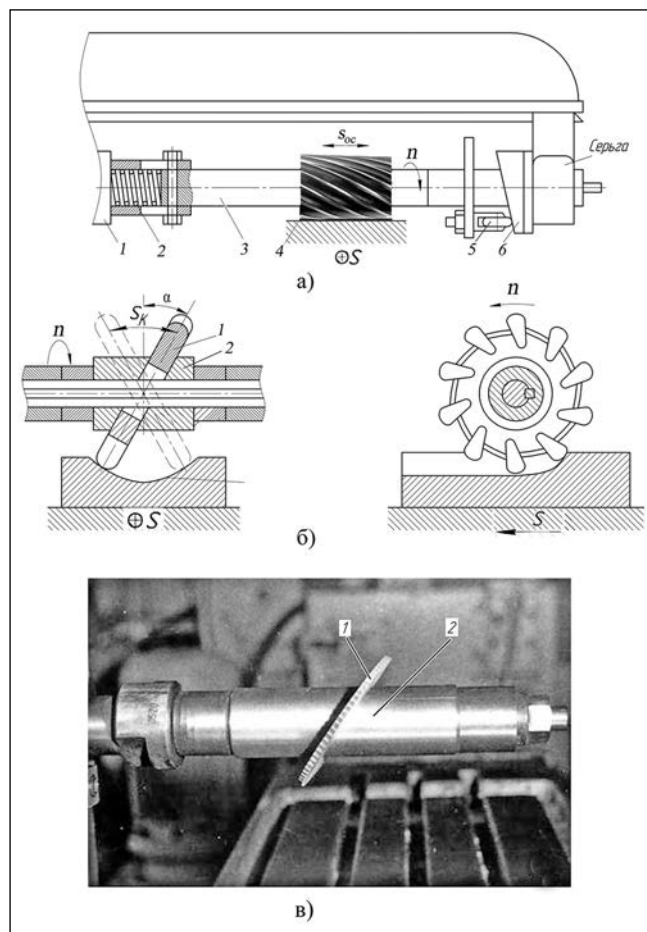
Фрезерование с дополнительной подачей: а) осевой, б) качательной, в) оправка с наклонной фрезой
